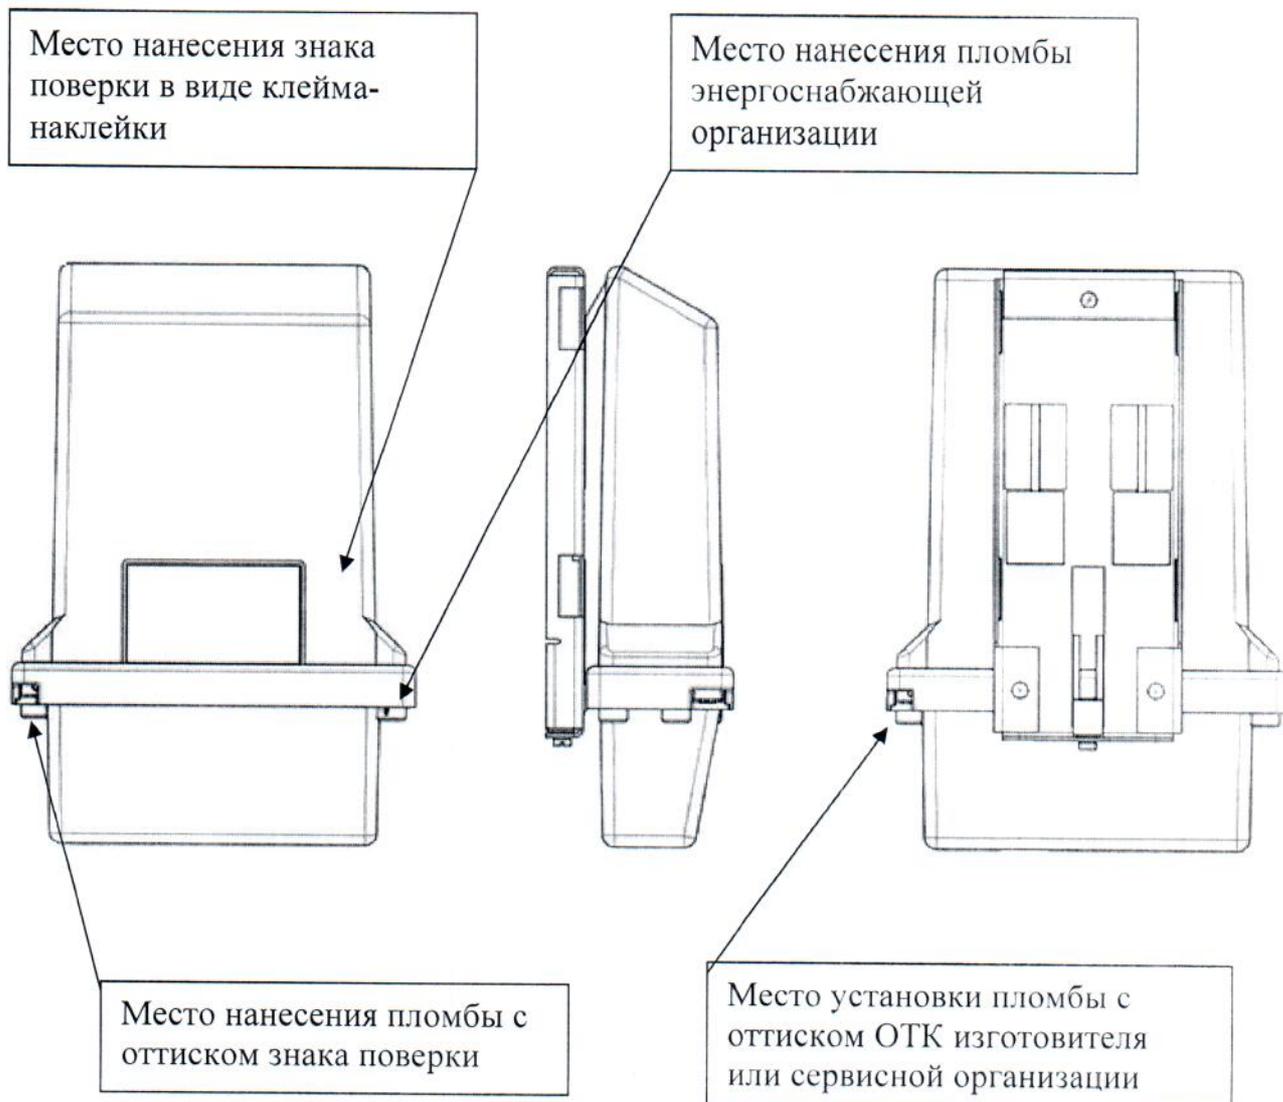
Схема (рисунок) с указанием места установки пломб и нанесения знака поверки в корпусе модификации SP1.
